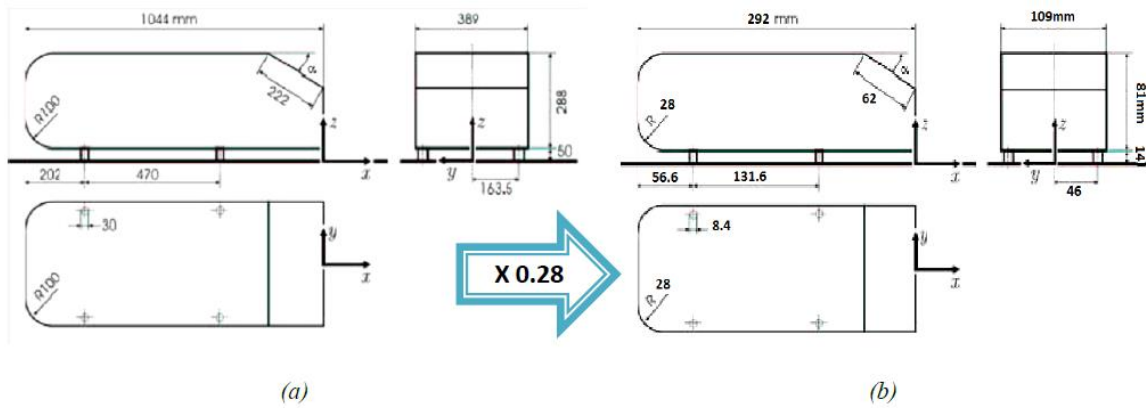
dessin de définition ((a) : dimensions d'Ahmed et al (b) : dimension de notre maquette)
